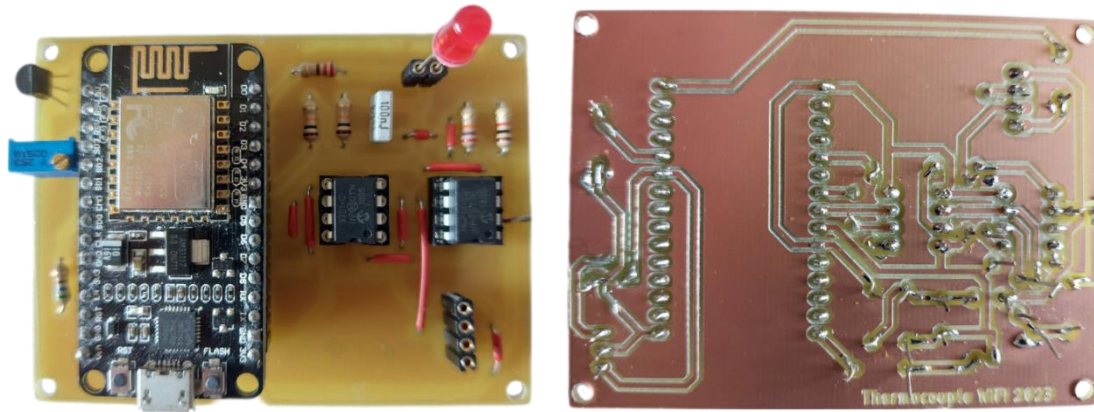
Photos du PCB après les soudures des connecteurs et l'ajout des composants.
